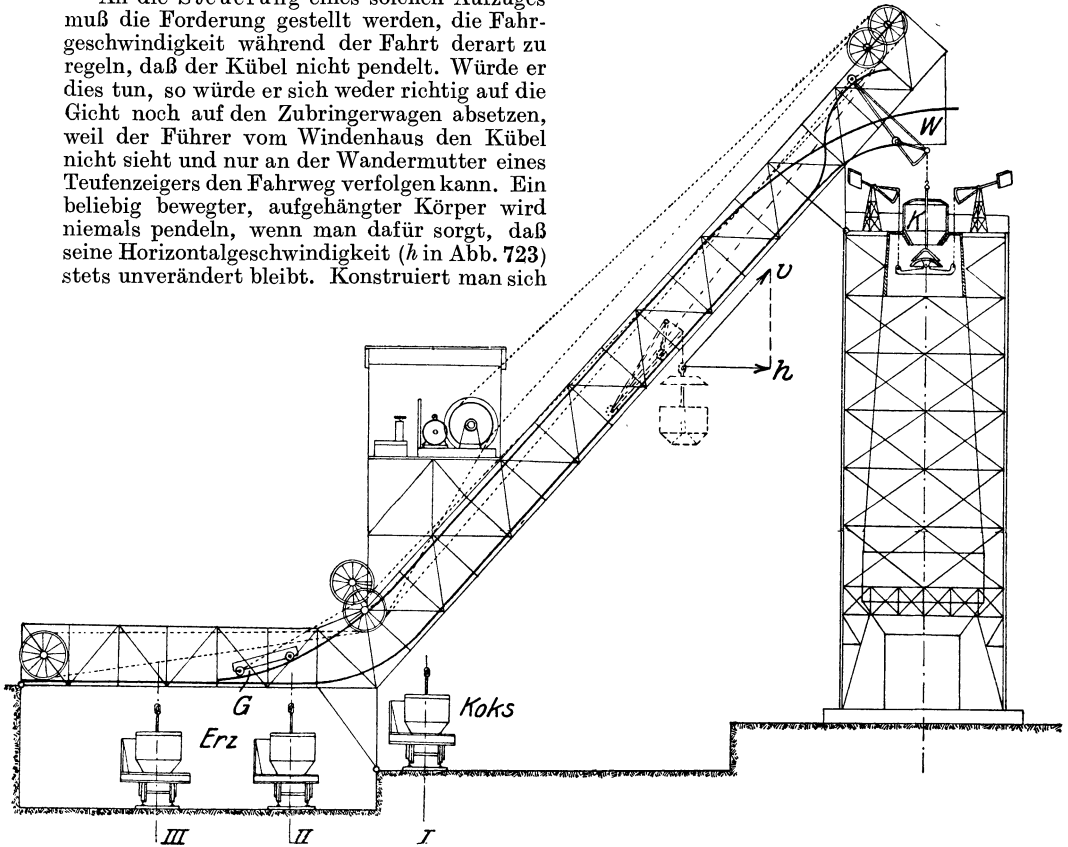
Hochofenschrägaufzug für Kübelförderung.
